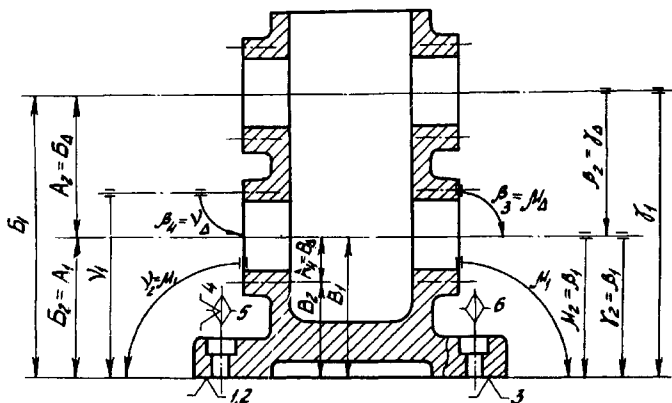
Схема базирования заготовки корпуса на большинстве операций
